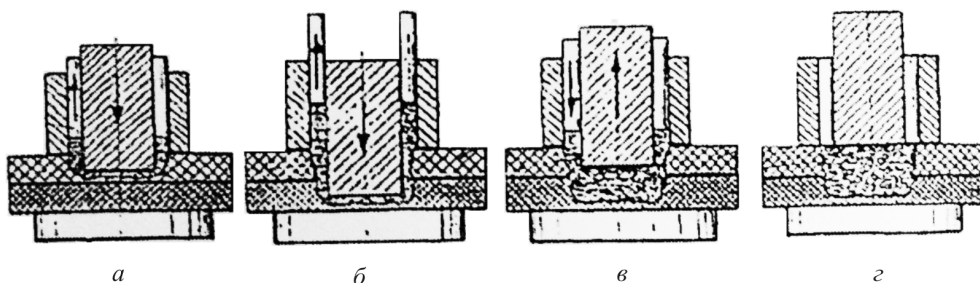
Схема ТСТП с заполнением шва: *а* – внедрение инструмента сплошного сечения в материал верхней детали; *б* – отвод инструмента несплошного сечения вверх; *в* – подача инструмента несплошного сечения вниз, отвод инструмента сплошного сечения; *г* – готовая сварная точка
